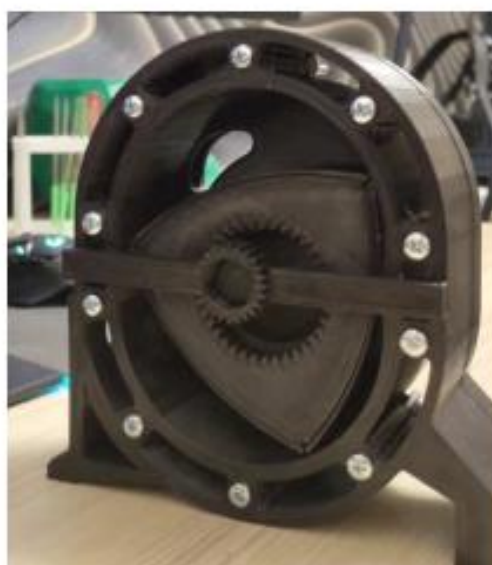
Распечатанная и работоспособная модель роторного двигателя Ванкеля
